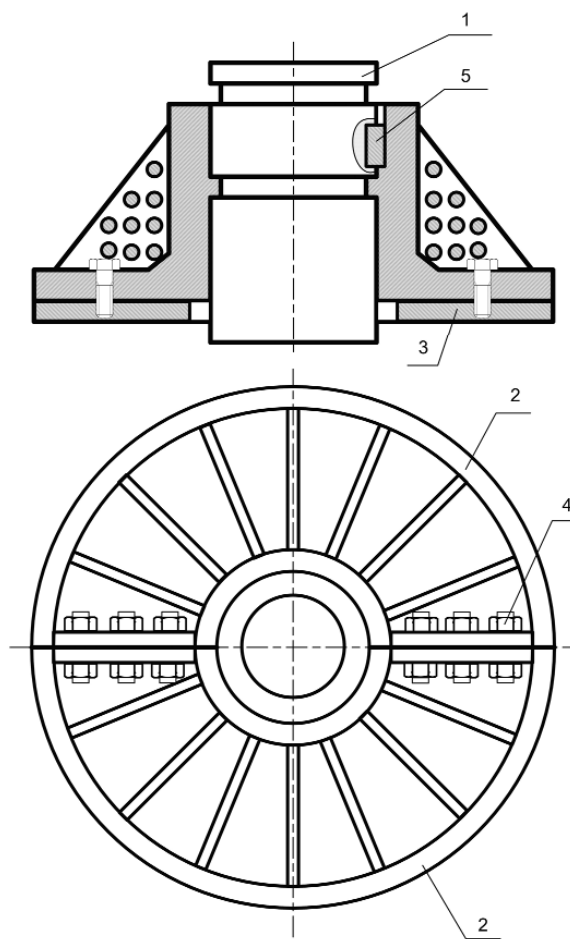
Втулка подпятника конструкции ГП "Электротяжмаш", 1 — вал ротора, 2 — половины втулка, 3 — диск, 4 — стяжные шпилеки, 5 — шпонка
